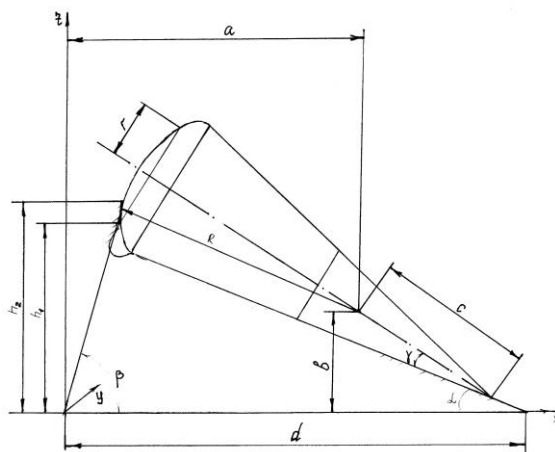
Контакт поверхонь торця ролика і опорного борта внутрішнього кільця
